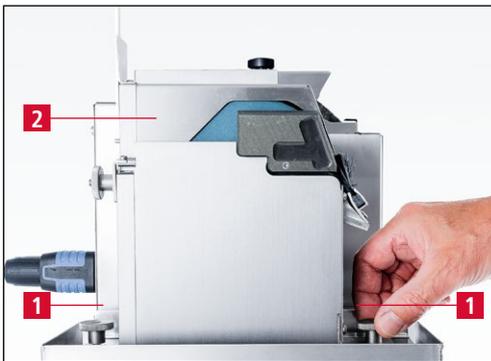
Desmontar la unidad de guiado de cuchillo
